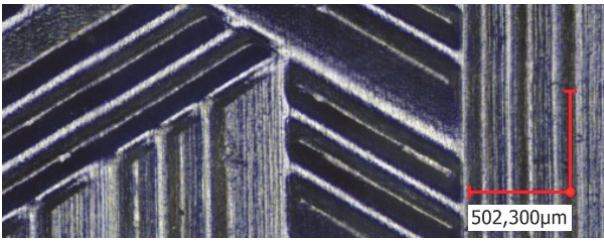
Draufsicht auf ein geprägtes Aluminiumblech mit 1 mm Dicke
